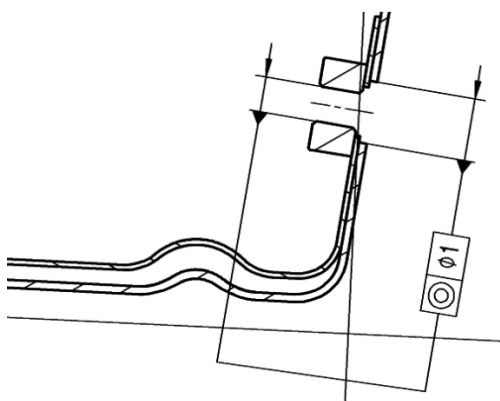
Pormenor da zona com furação roscada na lateral do conjunto, vista de topo e em corte
